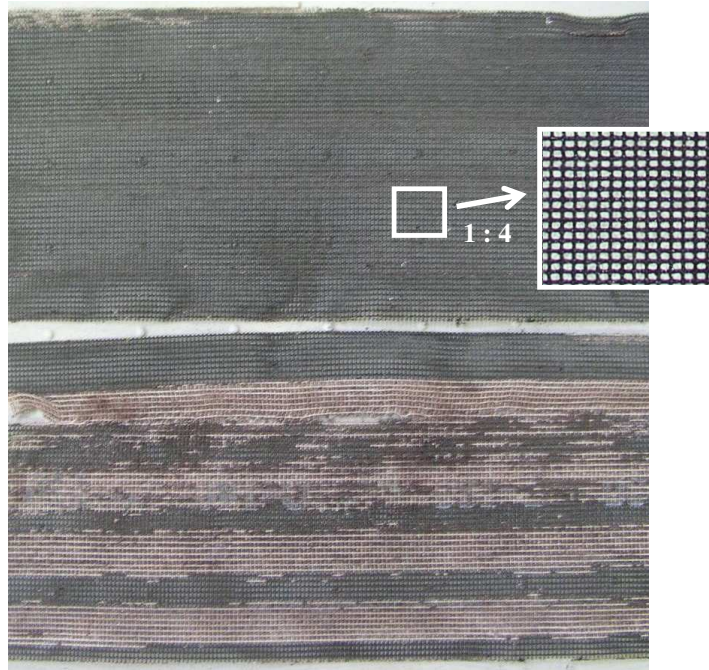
Schmirgelgewebe „Löwenzunge“ vor (oben, Detail) und nach einem Versuch (unten)
